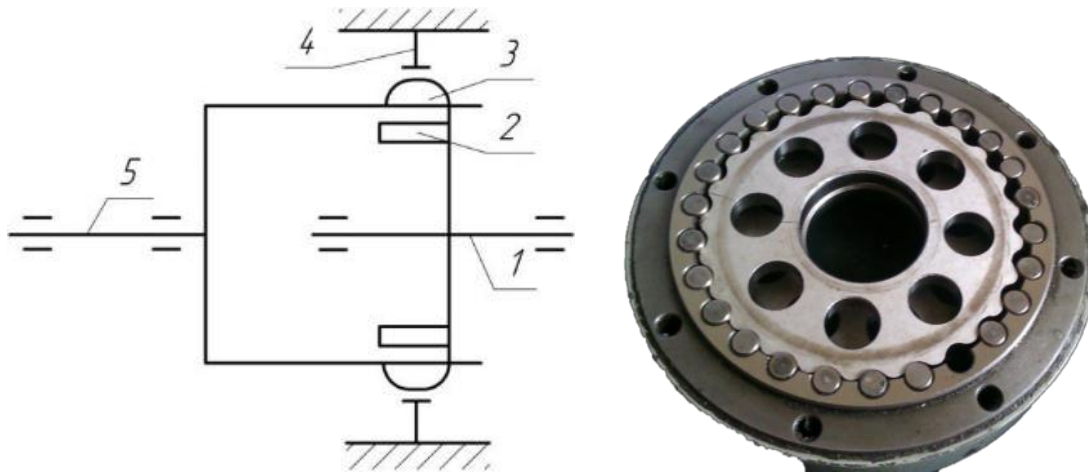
Волновой зубчатый одноступенчатый редуктор
